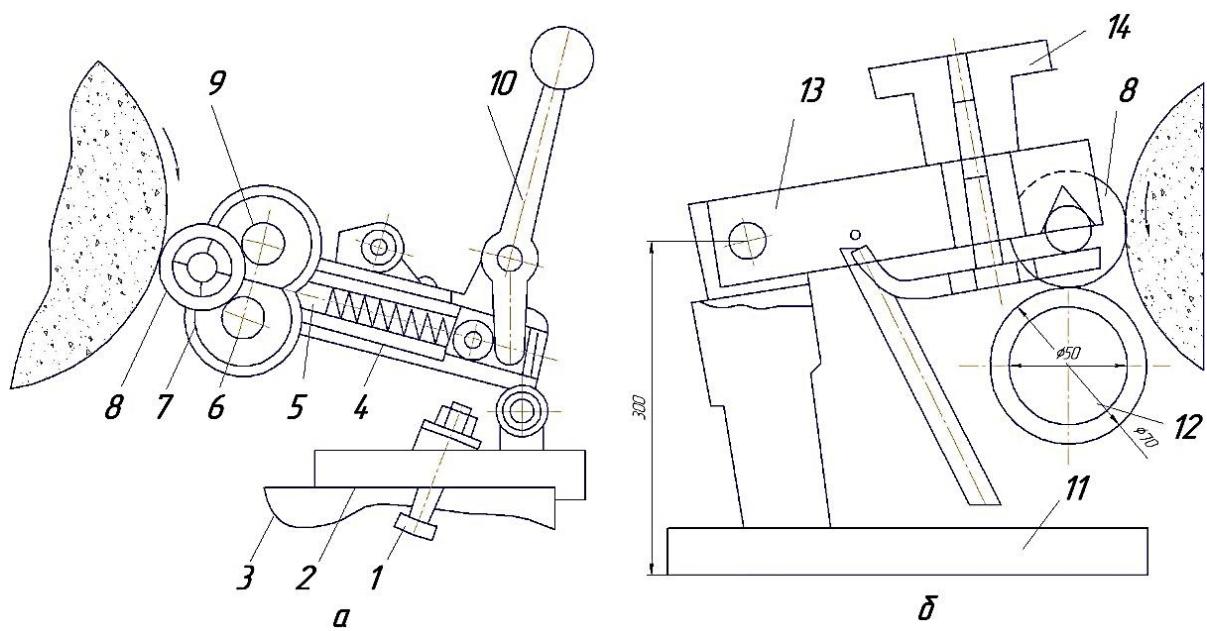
Приспособления для закрепления валика с подшипниками качения при шлифовании
